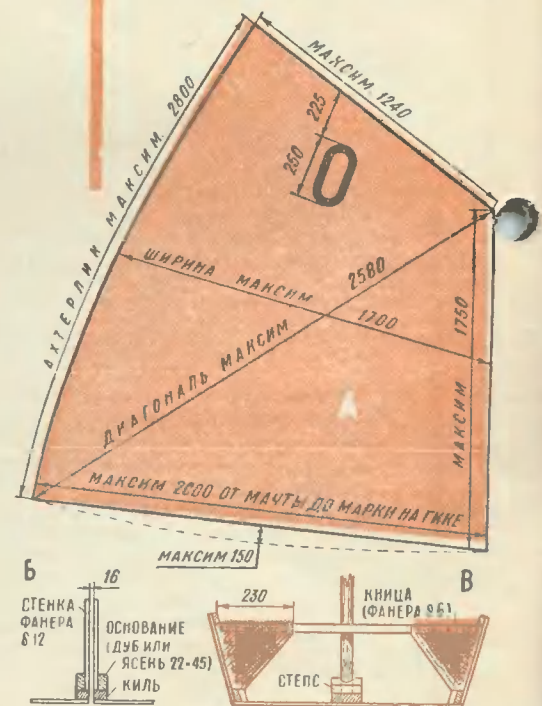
А — размеры паруса, Б — поперечный разрез по швертовому колодцу, В — поперечный разрез по банке.
